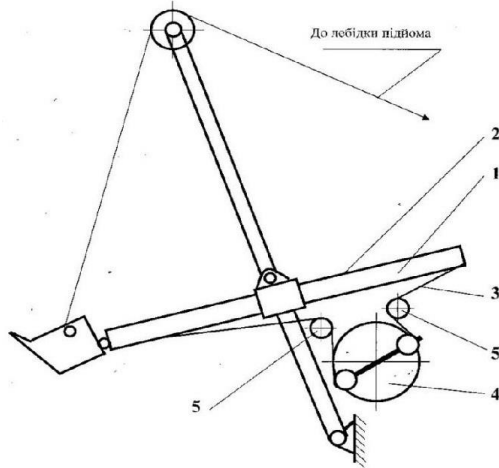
Конструктивна схема механізму натиску ковша екскаватора - прямої механічної лопати
